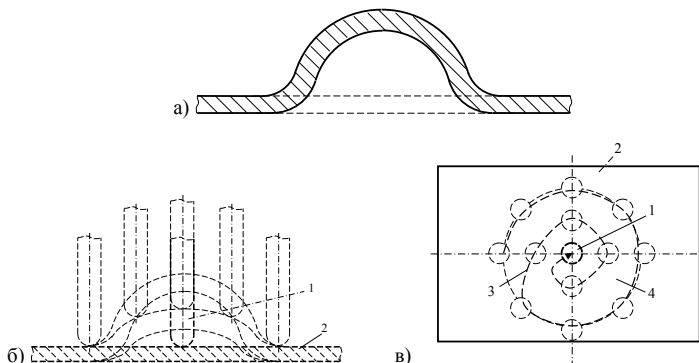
Принципова схема процесу відновлення початкової форми листової заготовки поетапним пластичним деформуванням
